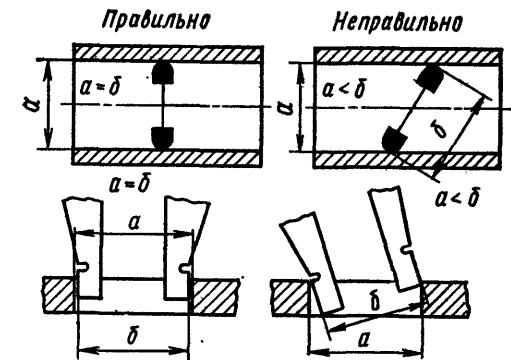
Установка штангенциркуля при измерении внутренних поверхностей
